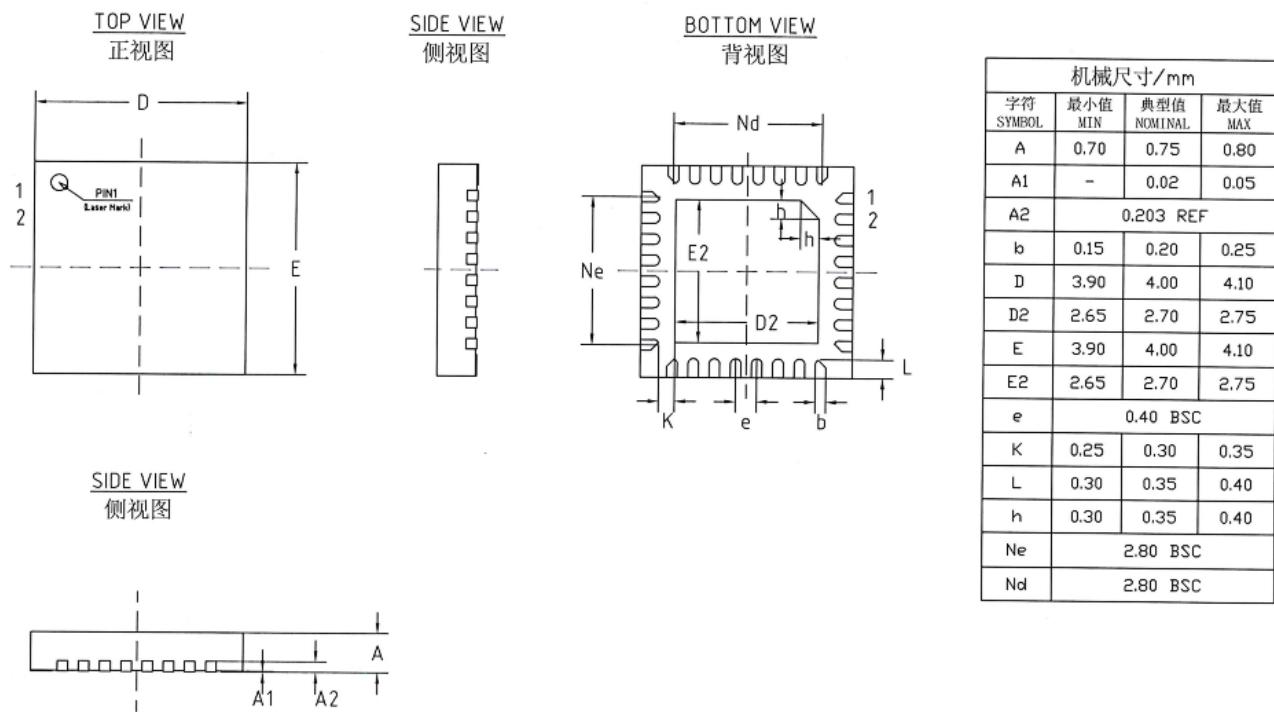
QFN32 (4*4*0.75-P0.4) 封装外形尺寸
